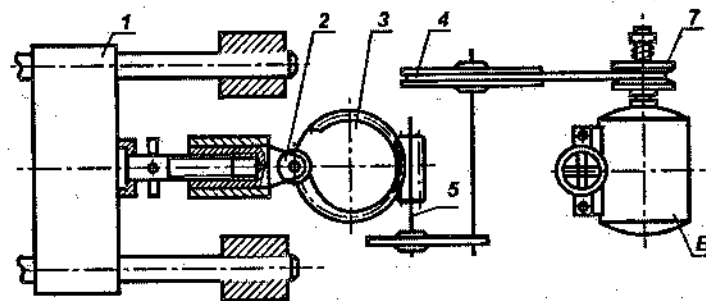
Механизм сжатия машин стыковой сварки с кулачковым электродвигательным приводом
